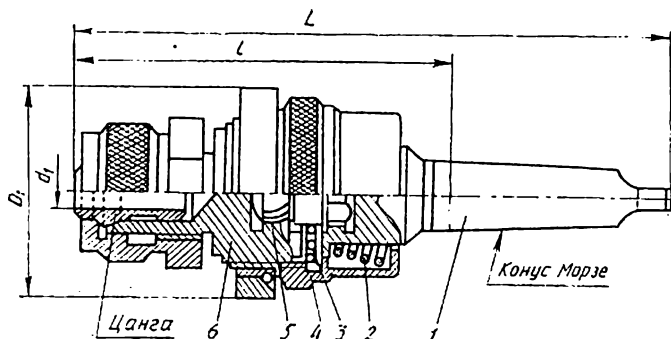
Гойдально-плавальний патрон для рорзвертки
